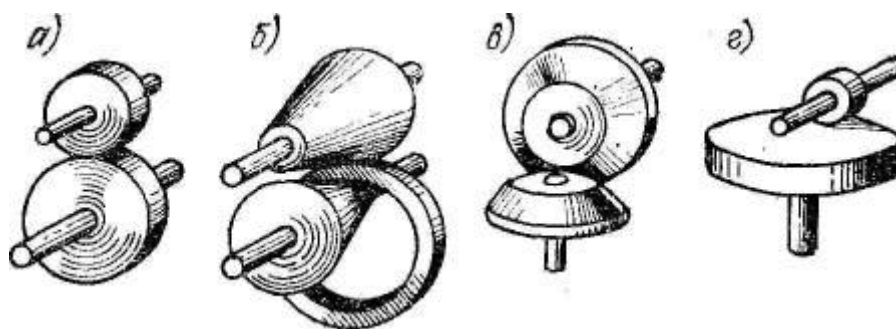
Фрикционные передачи: а – с параллельными осями – с цилиндрическими катками; б – с коническими; в – с пересекающимися осями – с коническими катками; г – с цилиндрическими катками – лобовая передача
